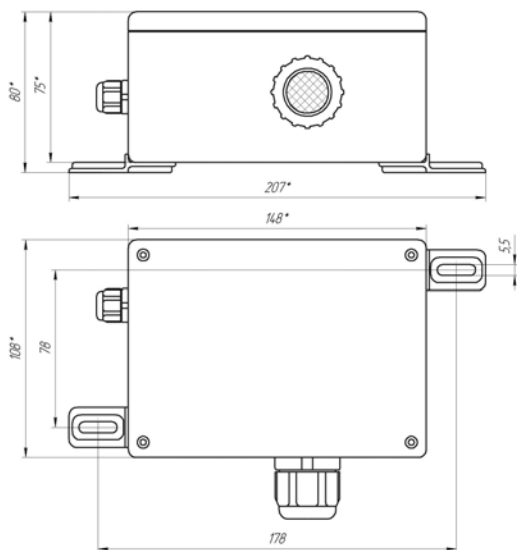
Габариты датчика в металлическом корпусе со встроенным сенсором (ФГИМ 413415.001-400-010-004)
